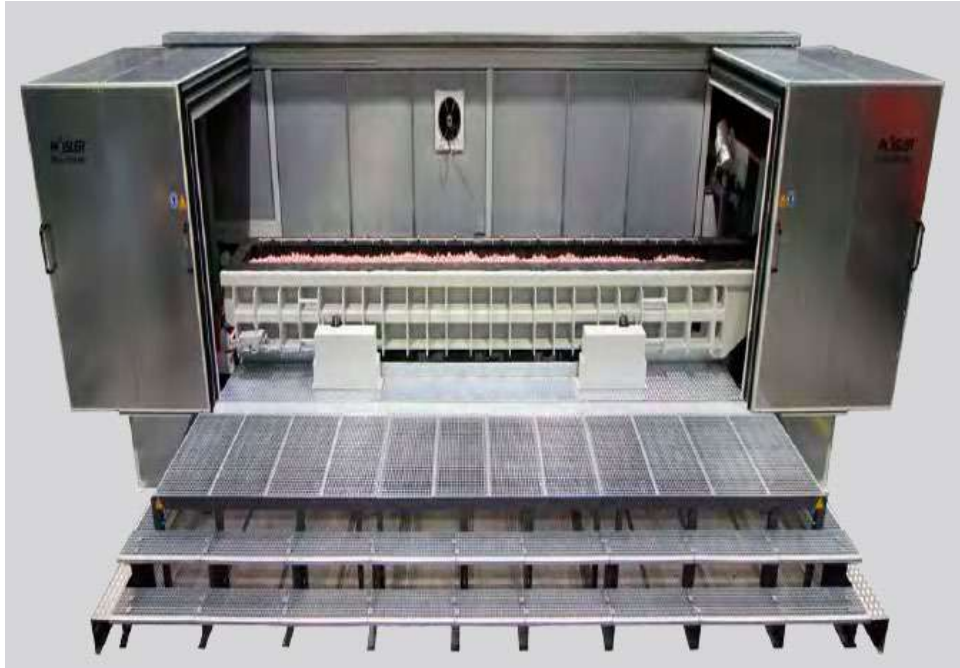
Лоткова установка для віброабразивної обробки
